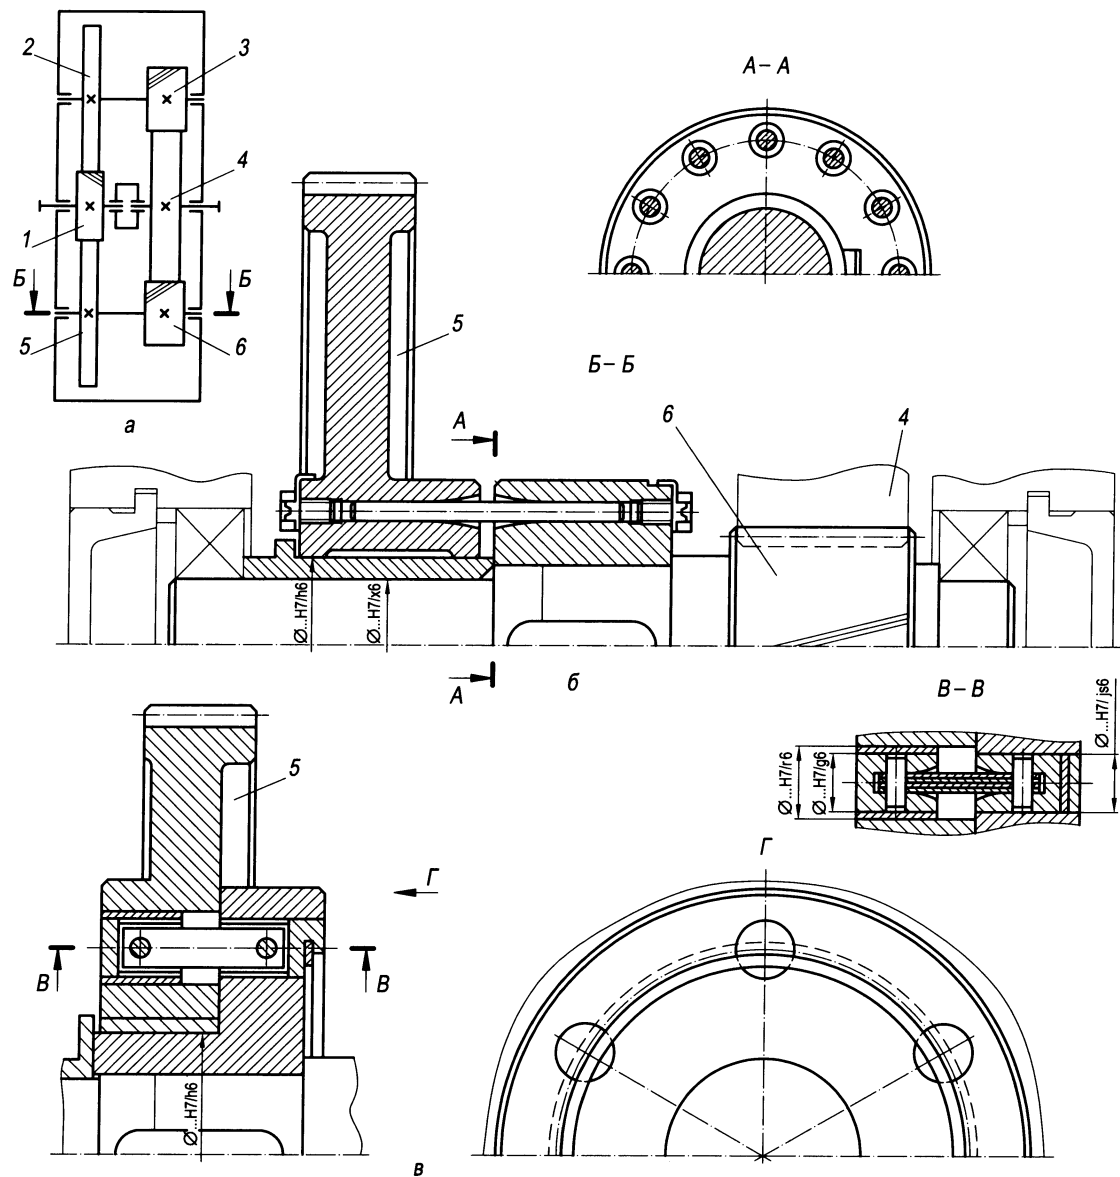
Кинематическая схема двухпоточного редуктора (а) и эскизы зубчатых колес быстрогоходной передачи со стержнями (б) и пакетами пластин (в), размещенными параллельно оси вала
